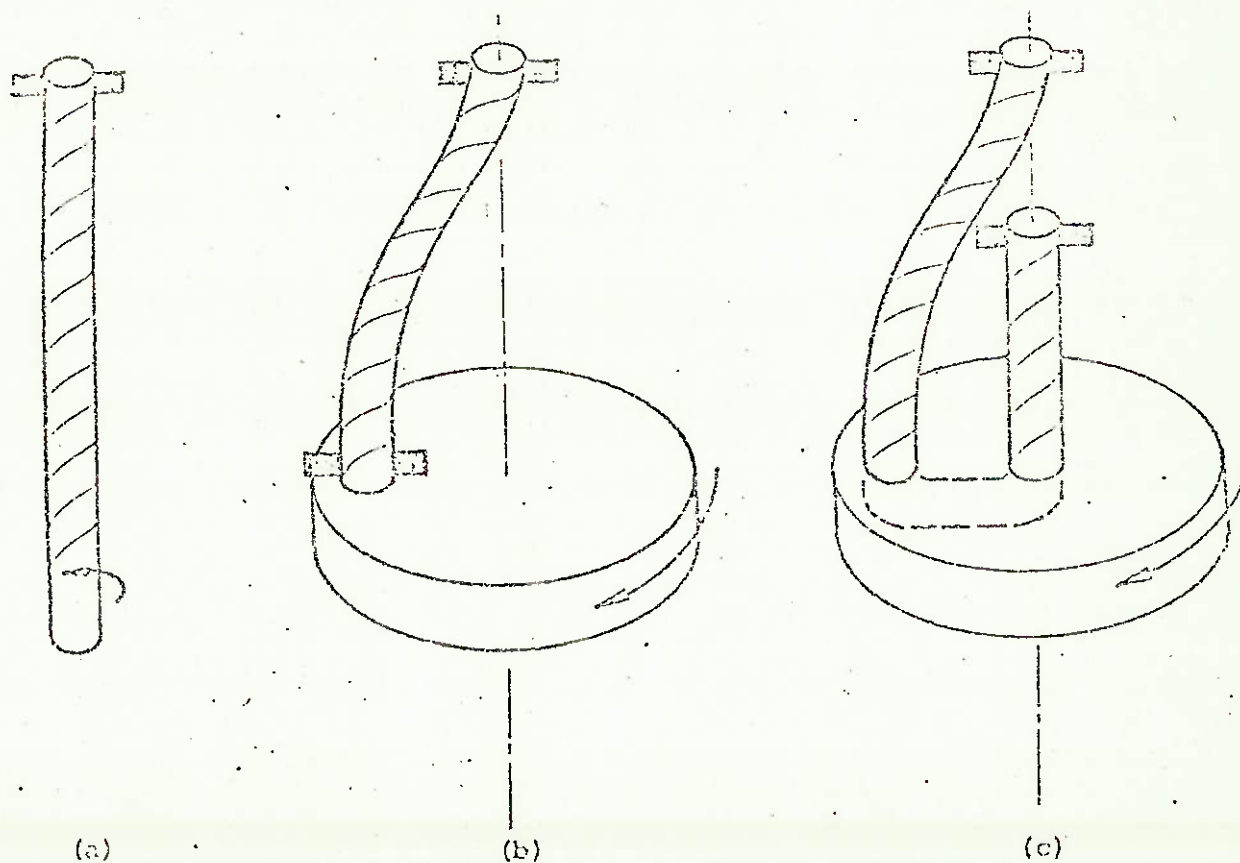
Princípio de Torcimento da Máquina de Dupla Torção
